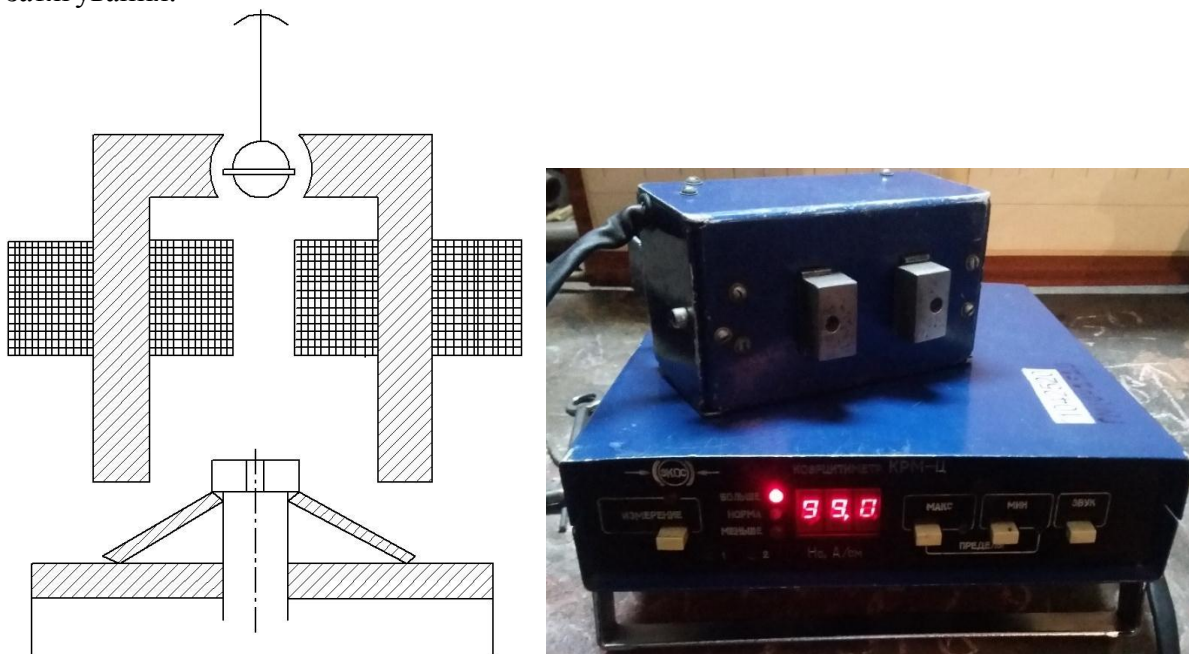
Вигляд різьбового з'єднання з конічною шайбою. Загальний вид датчика коерцитиметра
